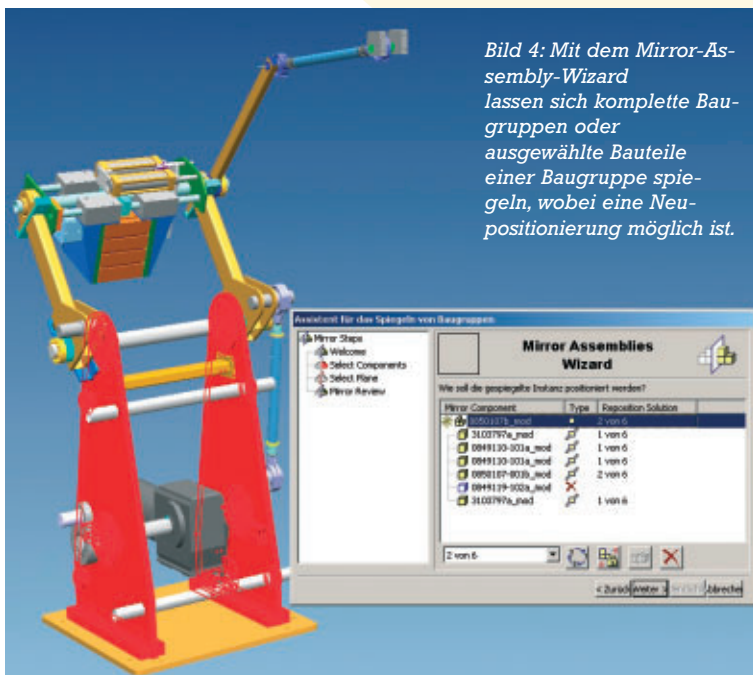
Mit dem Mirror-Assembly-Wizard lassen sich komplette Baugruppen oder ausgewählte Bauteile einer Baugruppe spiegeln, wobei eine Neupositionierung möglich ist.
